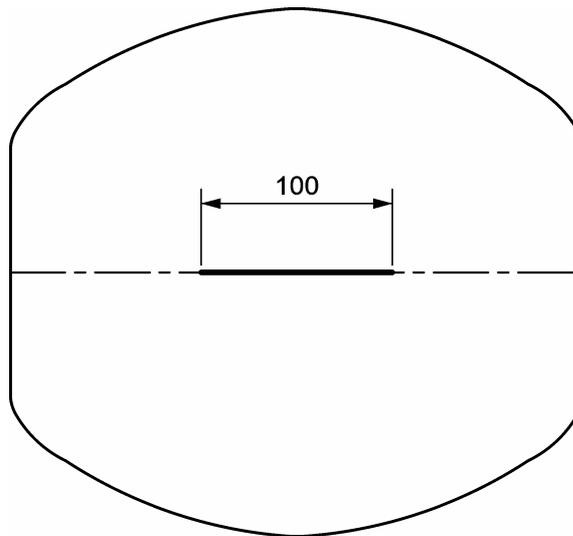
Umfang der Röntgenprüfung an Schweißnähten – Flaschen nur mit Rundnähten
